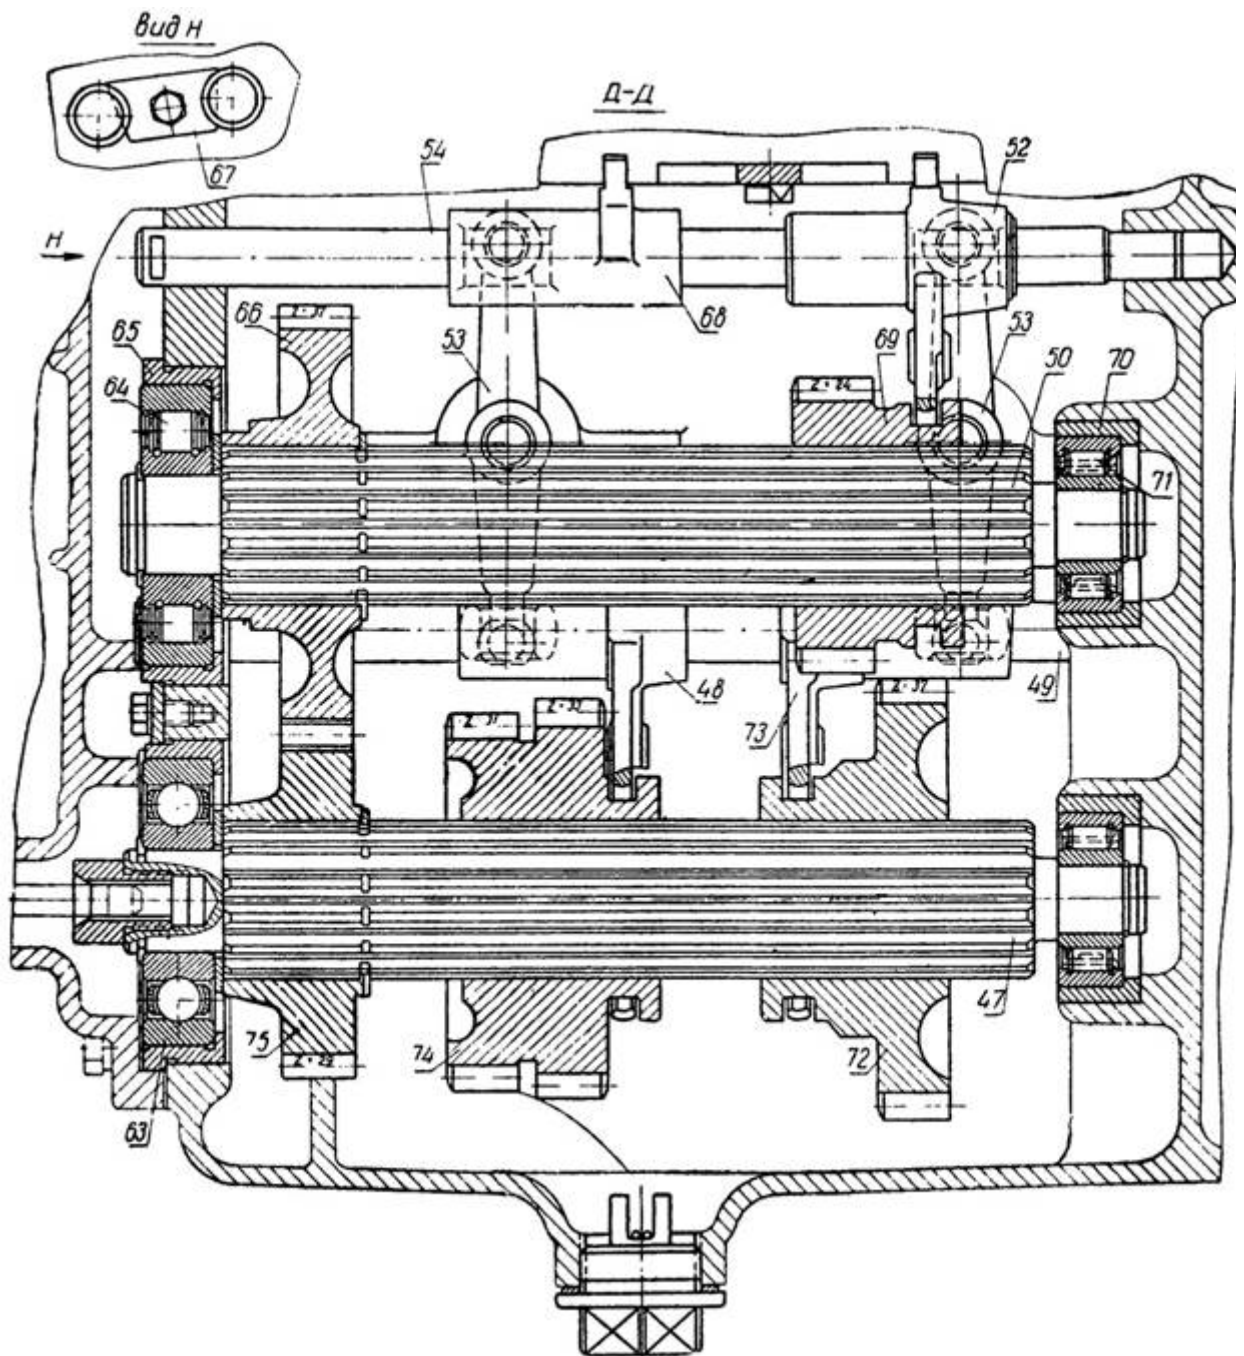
в. Коробка передач (разрез по валу заднего хода и дополнительному валу):
